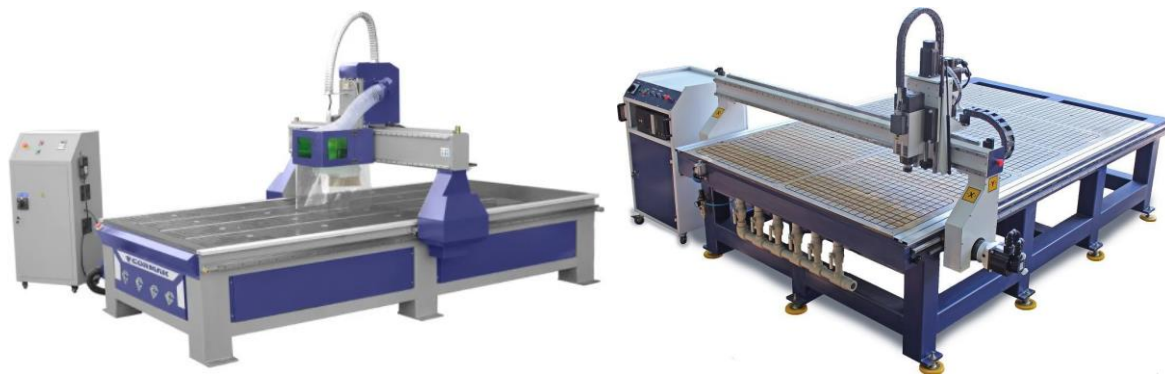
Загальний вигляд порталних фрезерних верстатів з ЧПК середнього рівня [15-16]
